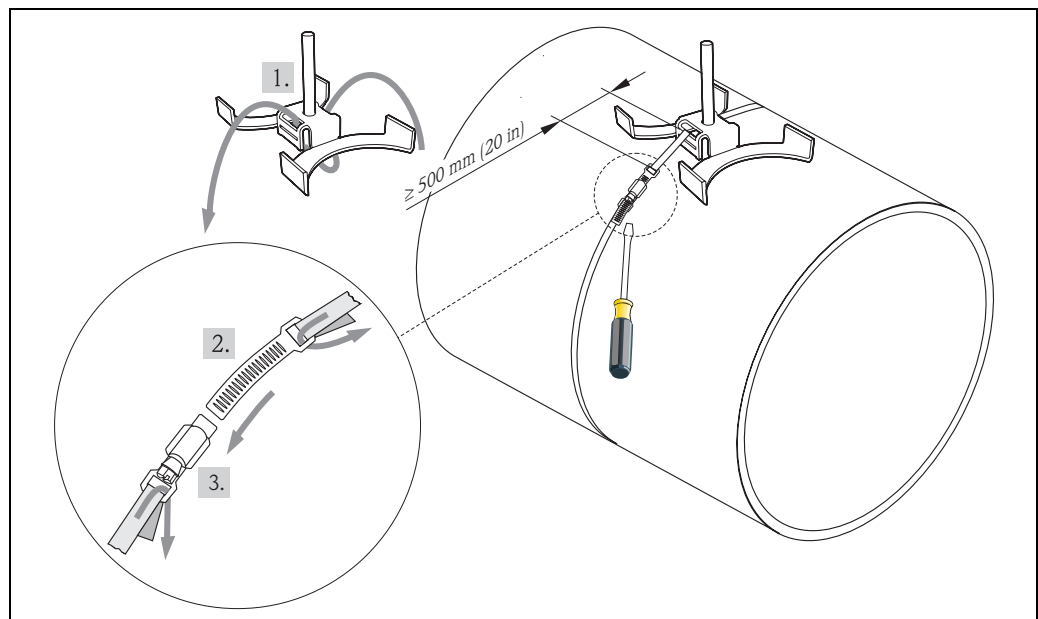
Premontaggio delle fascette di fissaggio per diametri del tubo DN > 600 (24 ")
